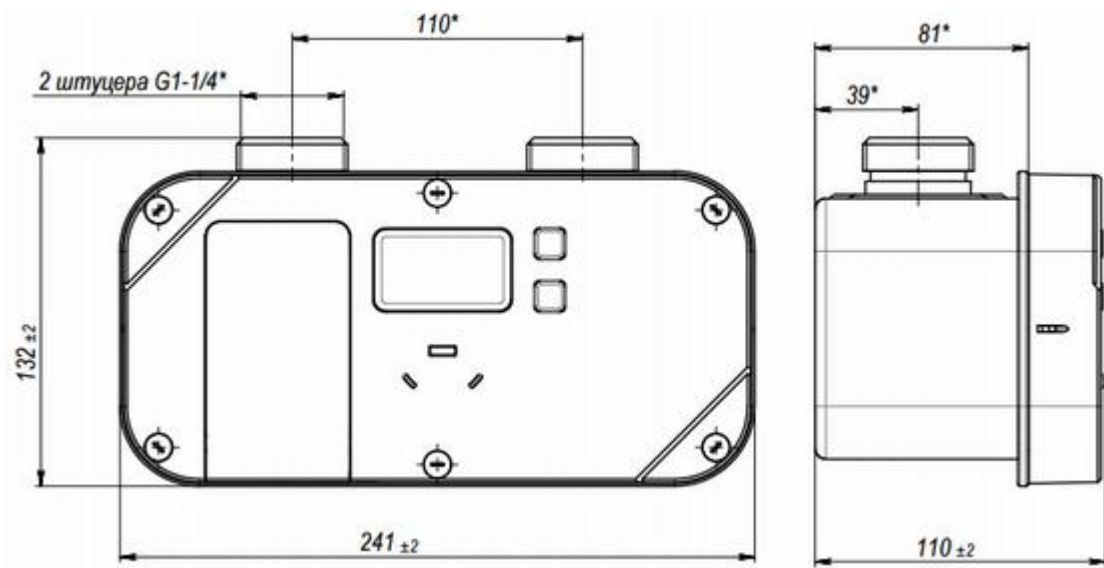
Тип корпуса F11, типоразмеры: G4, G6
